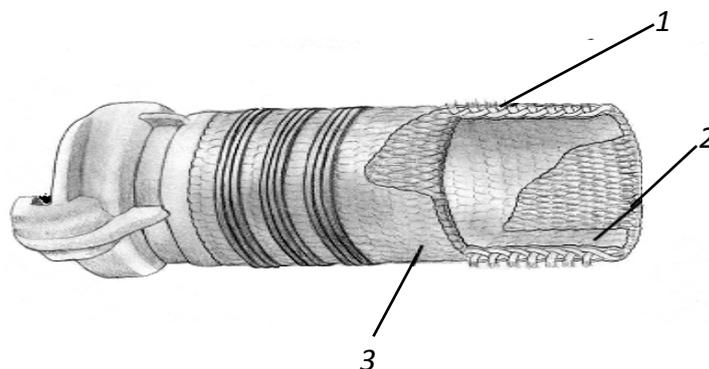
Конструкция напорного рукава с внутренним гидроизоляционным покрытием и пропиткой каркаса:
